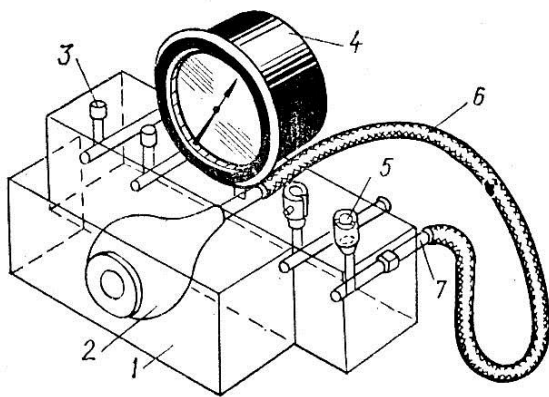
Прилад для перевірки герметичності голчастого клапана поплавкової камери:
